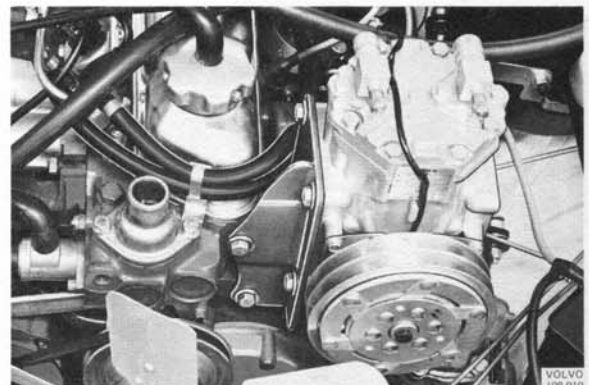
Kältemittelkompressor, eingebaut auf Motor B 20 E
